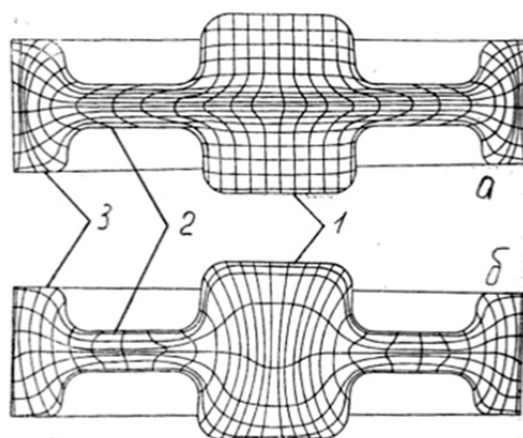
Характер течения металла при штамповке из заготовки деталей типа шестерни с  $H_0/D_0$ : а –  $\geq 2,0$ ; б –  $< 1,0$ ; 1 – ступица; 2 – диск; 3 – обод
